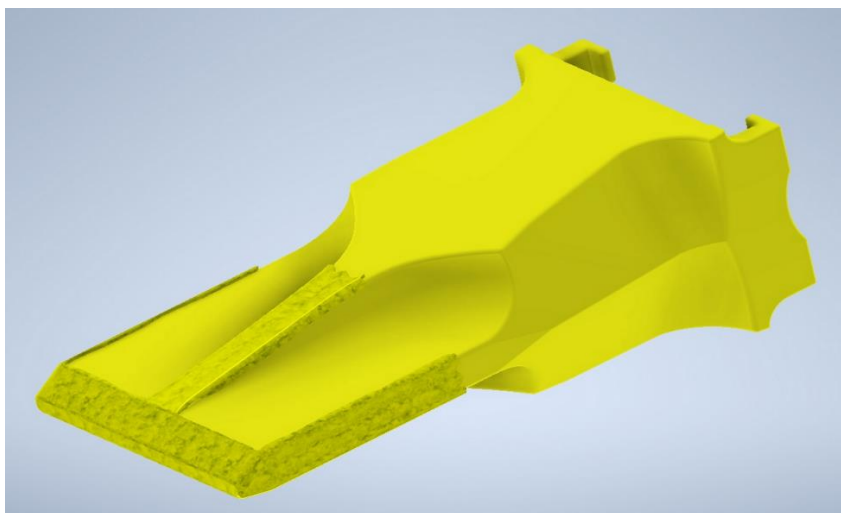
Зоны наплавки крупки на новую коронку экскаватора с покраской
